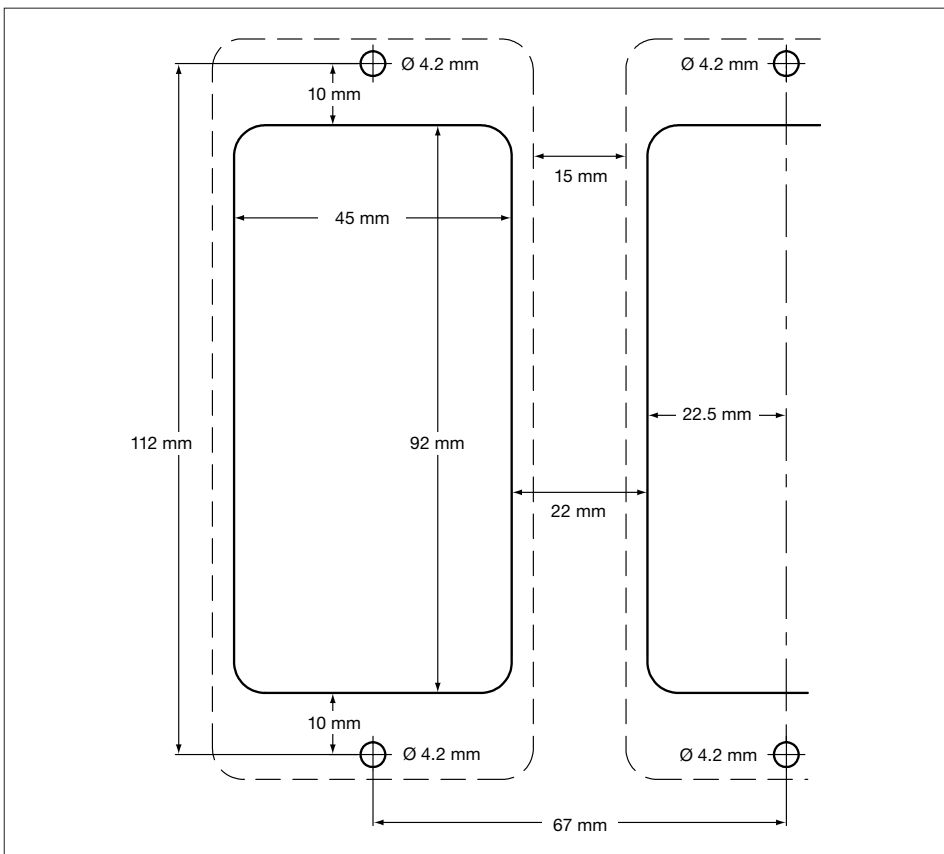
Montageschablone für Frontplattenmontage - Montage auf Montageplatte
